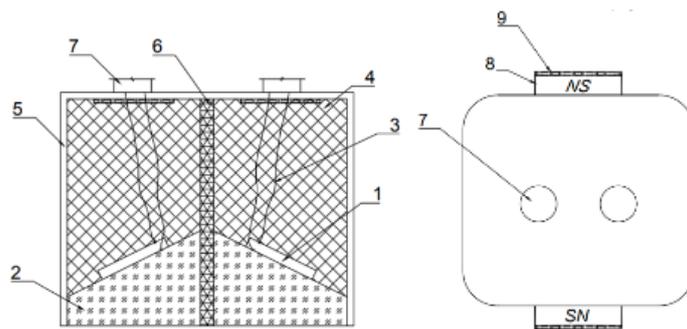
Конструкция ПЭП для разбраковки чугунов: 1 – пьезопластина; 2 – призма; 3 – проводники; 4 – демпфер; 5 – корпус; 6 – звукоизолирующая перегородка; 7 – разъем; 8 – магниты; 9 – магнитопровод
